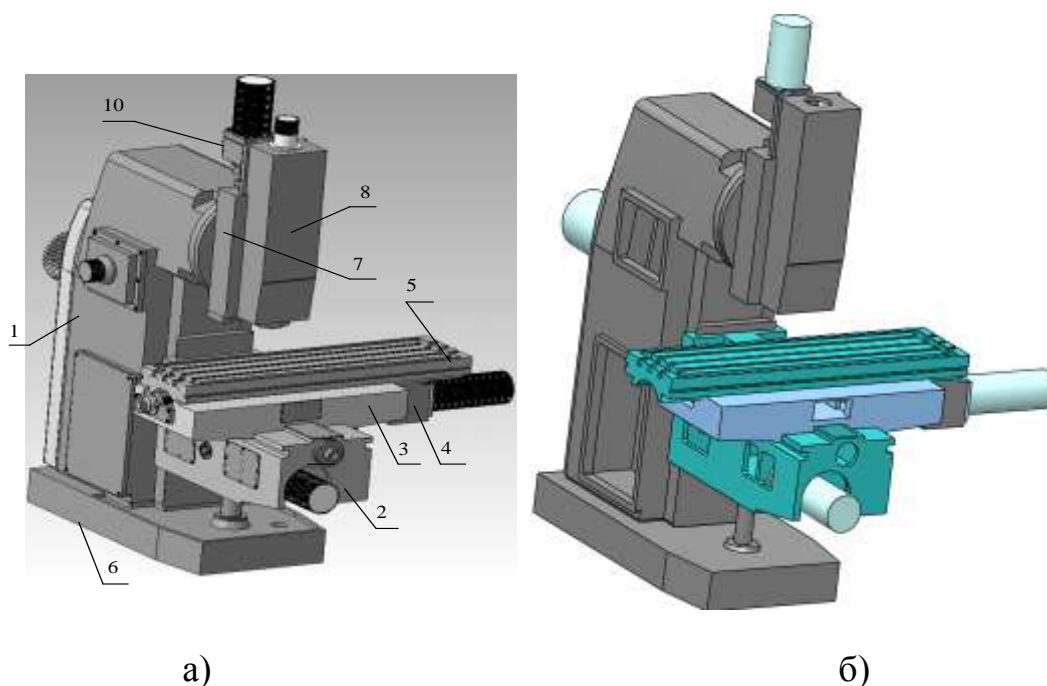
3-D моделі вертикально-фрезерного верстата:
